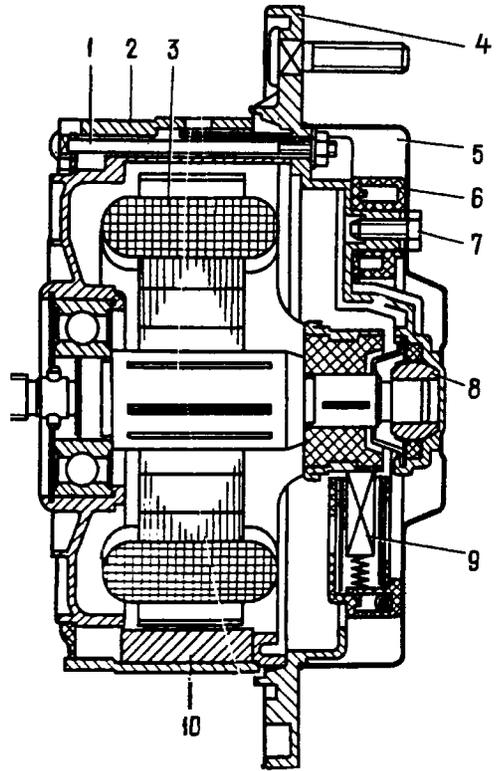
Электродвигатель вентилятора системы охлаждения двигателя: 1 - стяжной болт; 2 - корпус; 3 - якорь; 4 - крышка; 5 - кожух; 6 - щеткодержатель; 7 - болт крепления щеткодержателя; 8 - втулка подшипника якоря; 9 - щетка; 10 - полюс (постоянный магнит)
